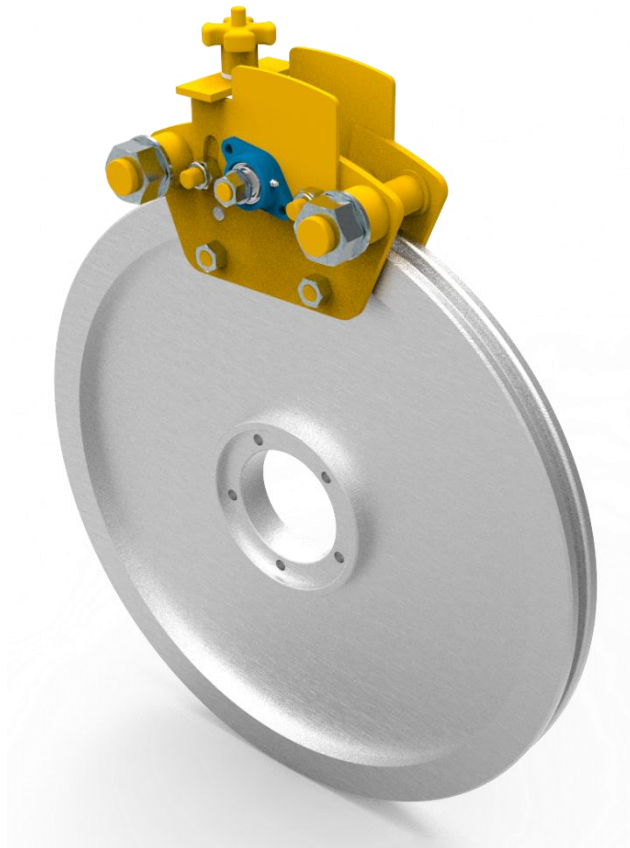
Equipamento aplicado a roda de Ø800mm.
